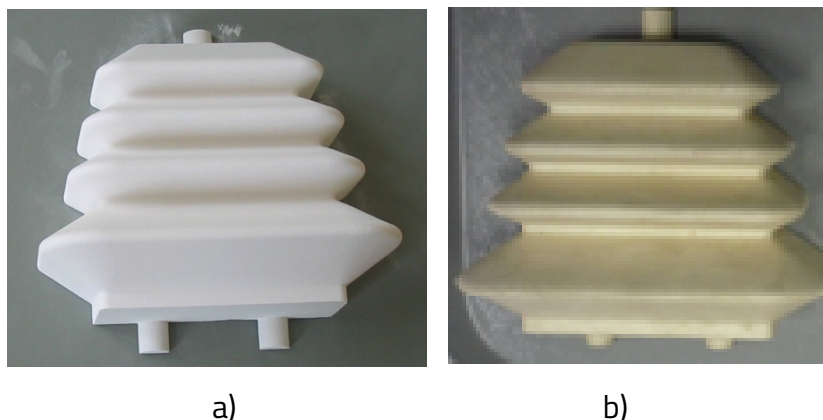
Calapodul burdufului: a) în stare crudă; b) după infiltrare cu rășină [24]
